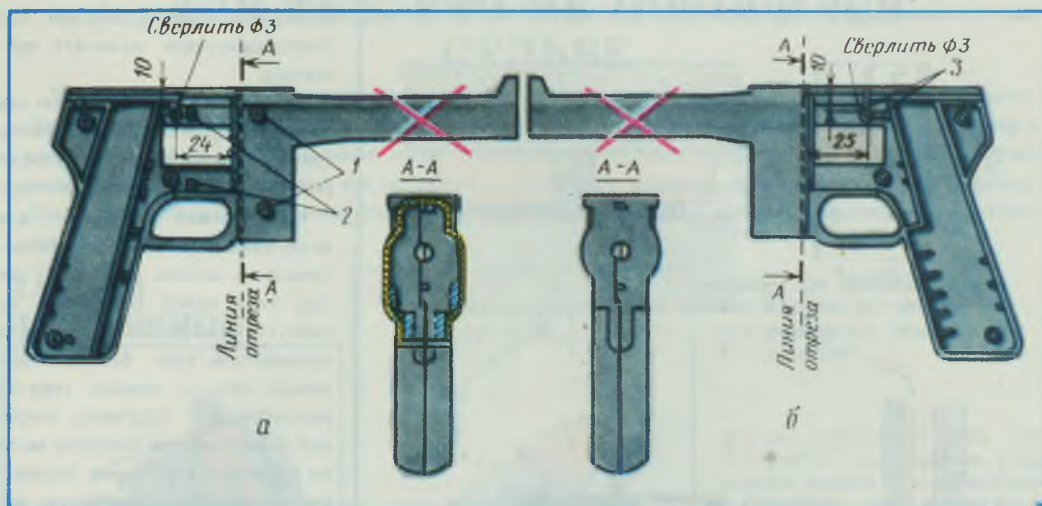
Изготовление электроточила из детского пистолета (а — основание корпуса; б — крышка корпуса): 1 — выступы; 2 — прокладки; 3 — перегородки.
